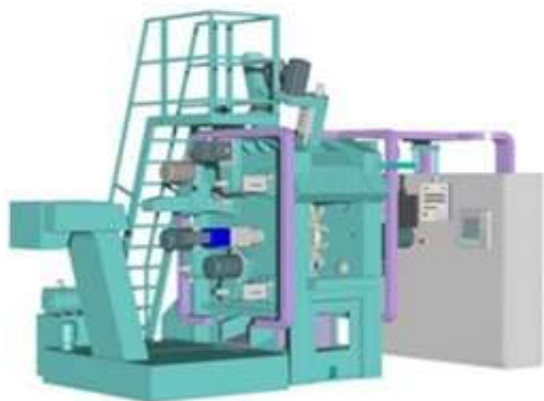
Компоновка агрегатного станка с поворотным барабаном VIGNOTTO Vi03
